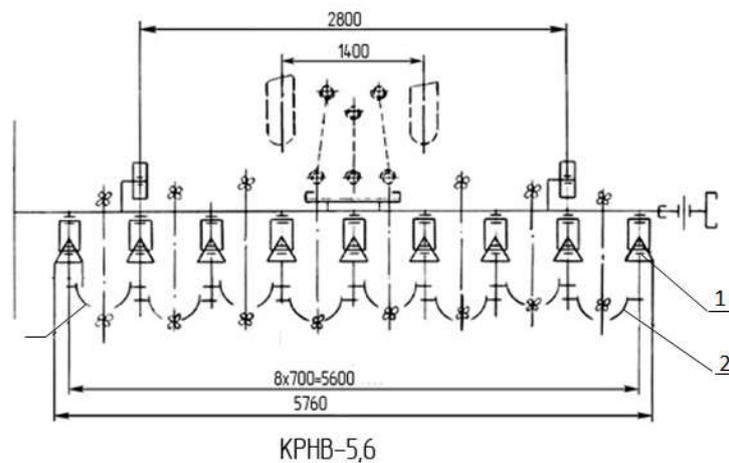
Схема розташування робочих органів під час роботи з лапами-підгортачами для міжрядь 70 см:
